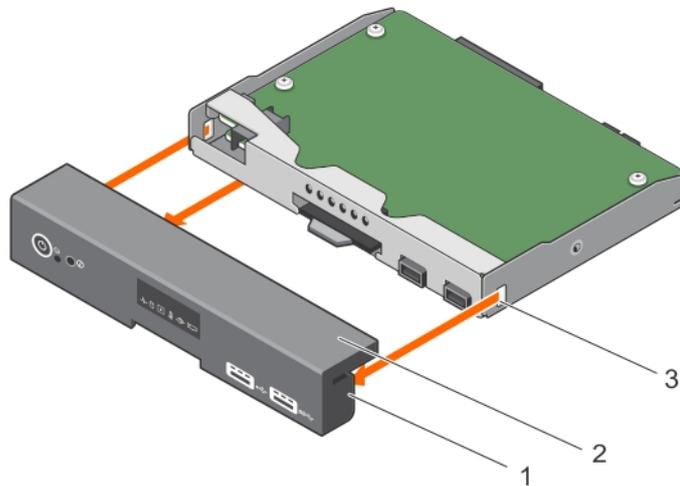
Extracción de la cubierta del ensamblaje del panel de control para un sistema con panel LED.
